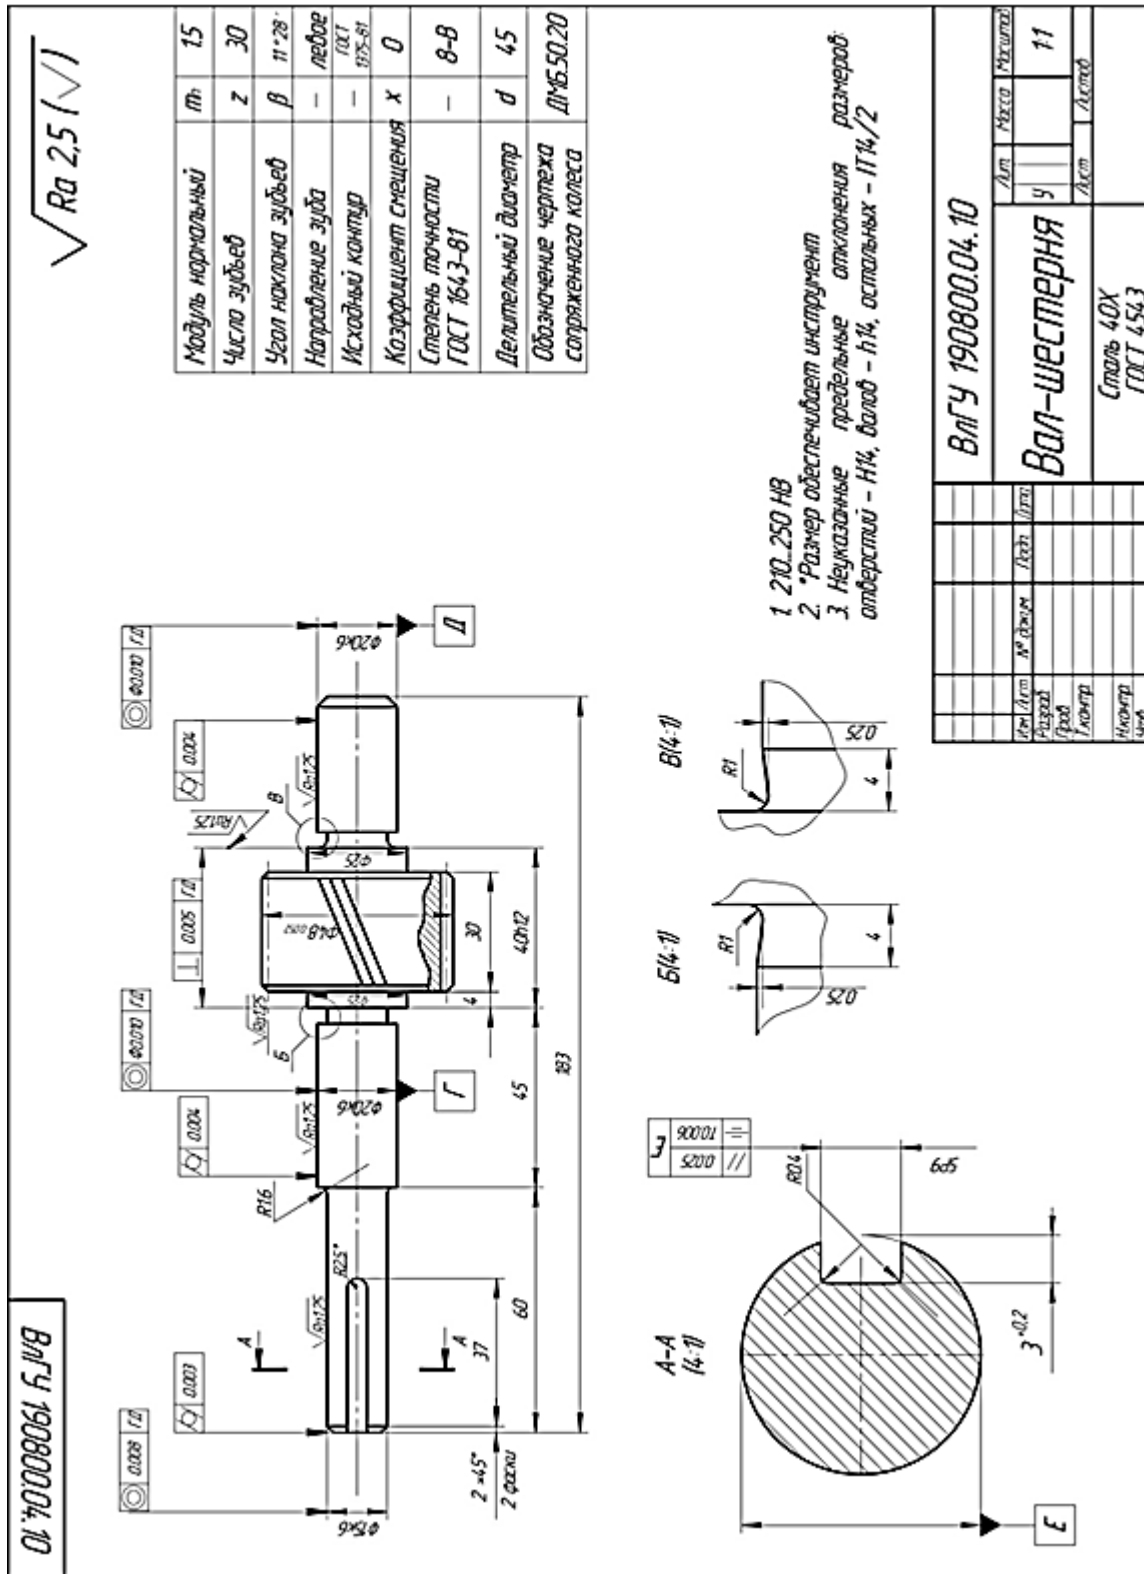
Рабочий чертеж вала (после исправления ошибок)
